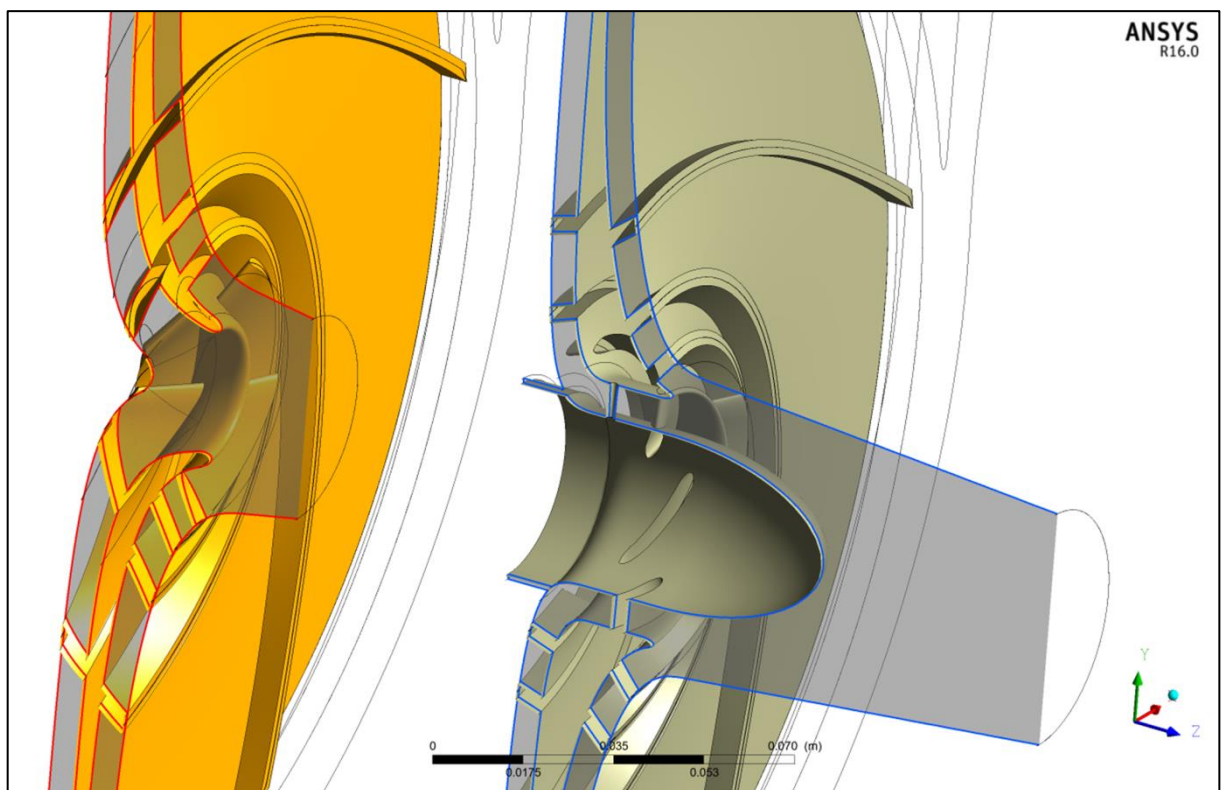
3d- Ansicht der Gegenüberstellung der Pumpenvariante für die mechanische Fertigung (rechts) und für die gusstechnische Fertigung (links)
